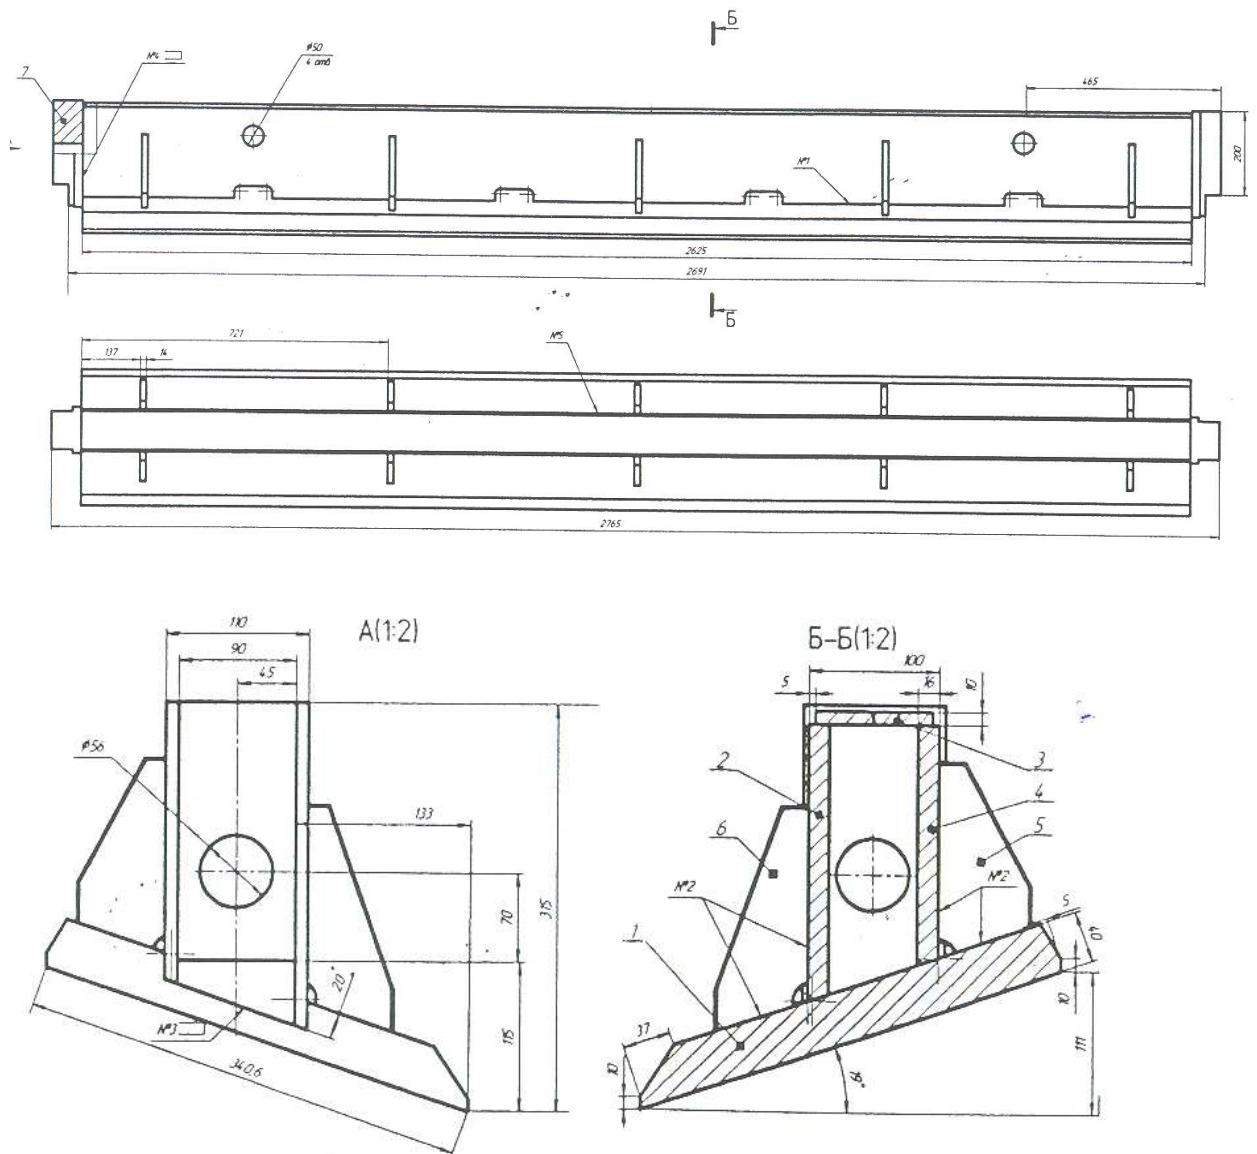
Загальний вид поперечної балки платформи скраповозу.
